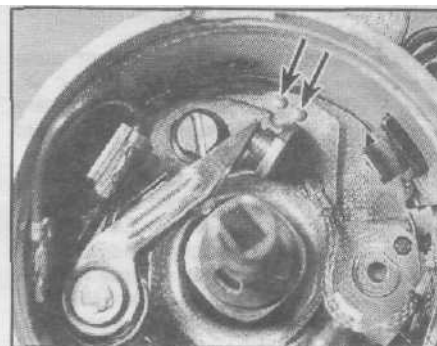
, в. Две заклепки и паз (показаны стрелками) для установки отвертки при регулировке зазора между контактами прерывателя
